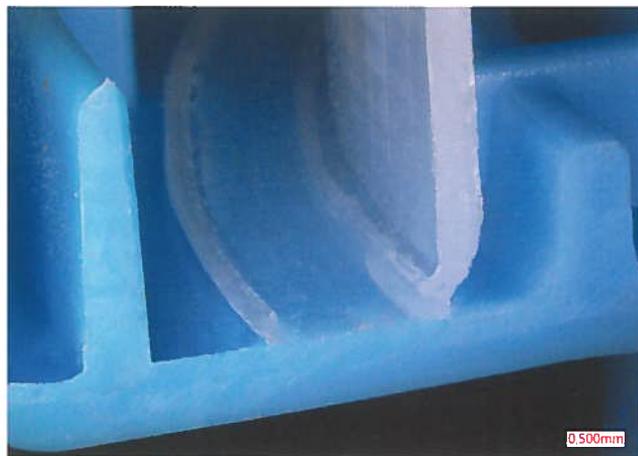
Umlaufende Schweißnaht: Ein runder blauer Deckel wird auf einen durchsichtigen Sekretbehälter geschweißt © Herrmann Ultraschall
